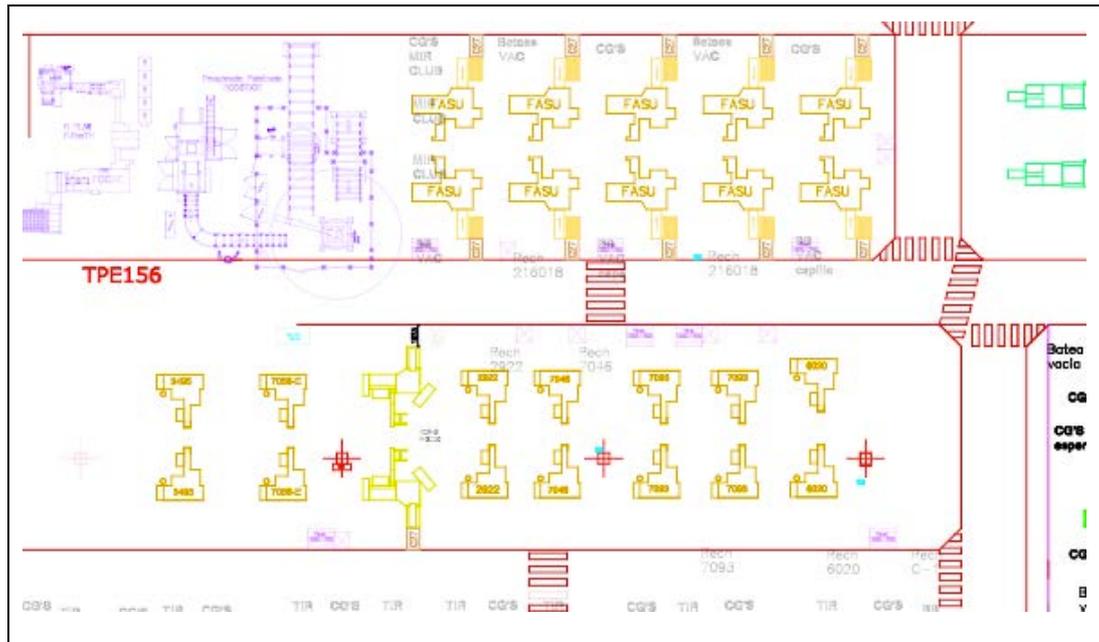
Plano detalle de la zona 1 entera y parte de zona 2 de liadoras. [Fuente: Elaboración propia]
